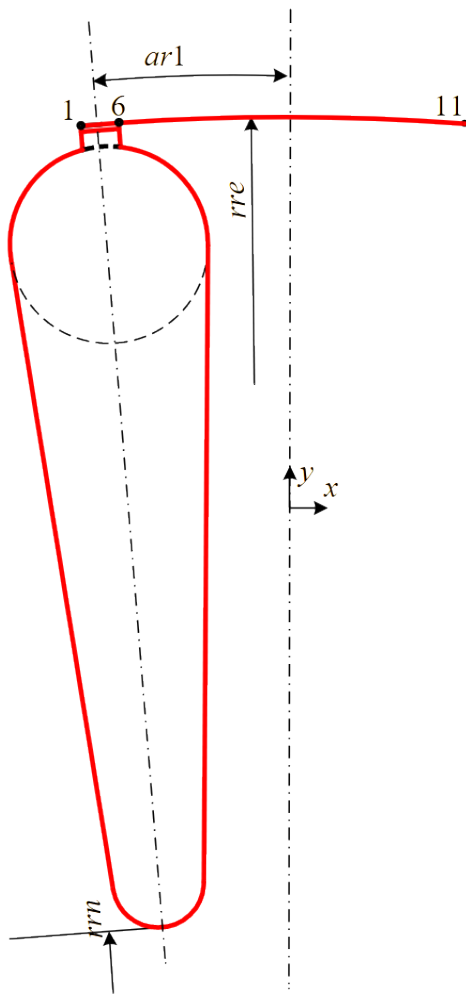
Повернутий зубцевий крок ротора для його копіювання
